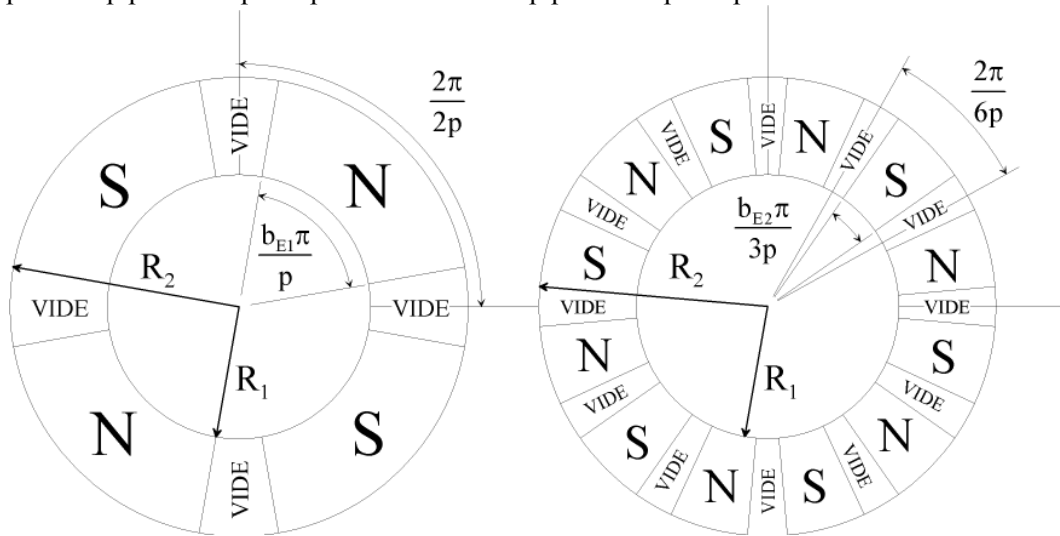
Rotor 1 et 2 de la machine à flux axial (vue de face)
